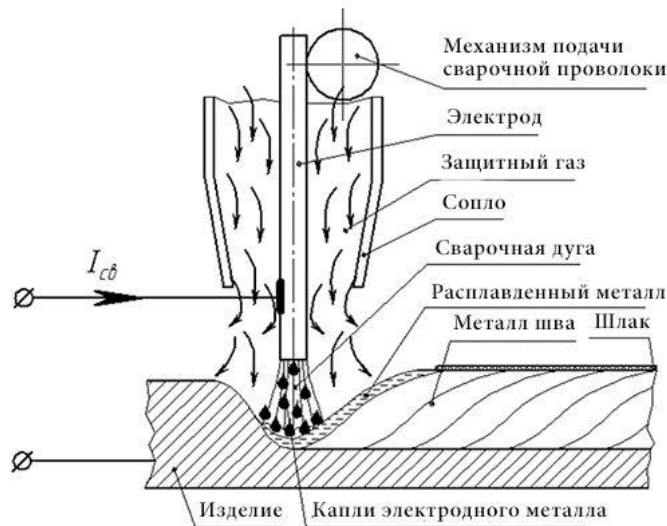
Схема осуществления механизированной сварки в среде защитного газа
